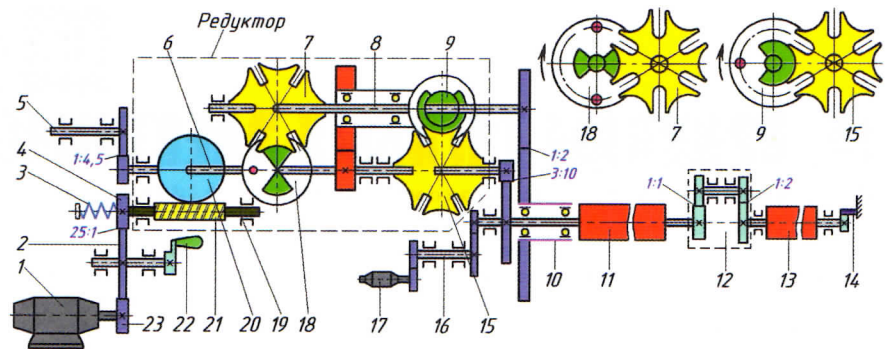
Кинематическая схема главного контроллера ЭКГ-8 с электродвигательным приводом:
